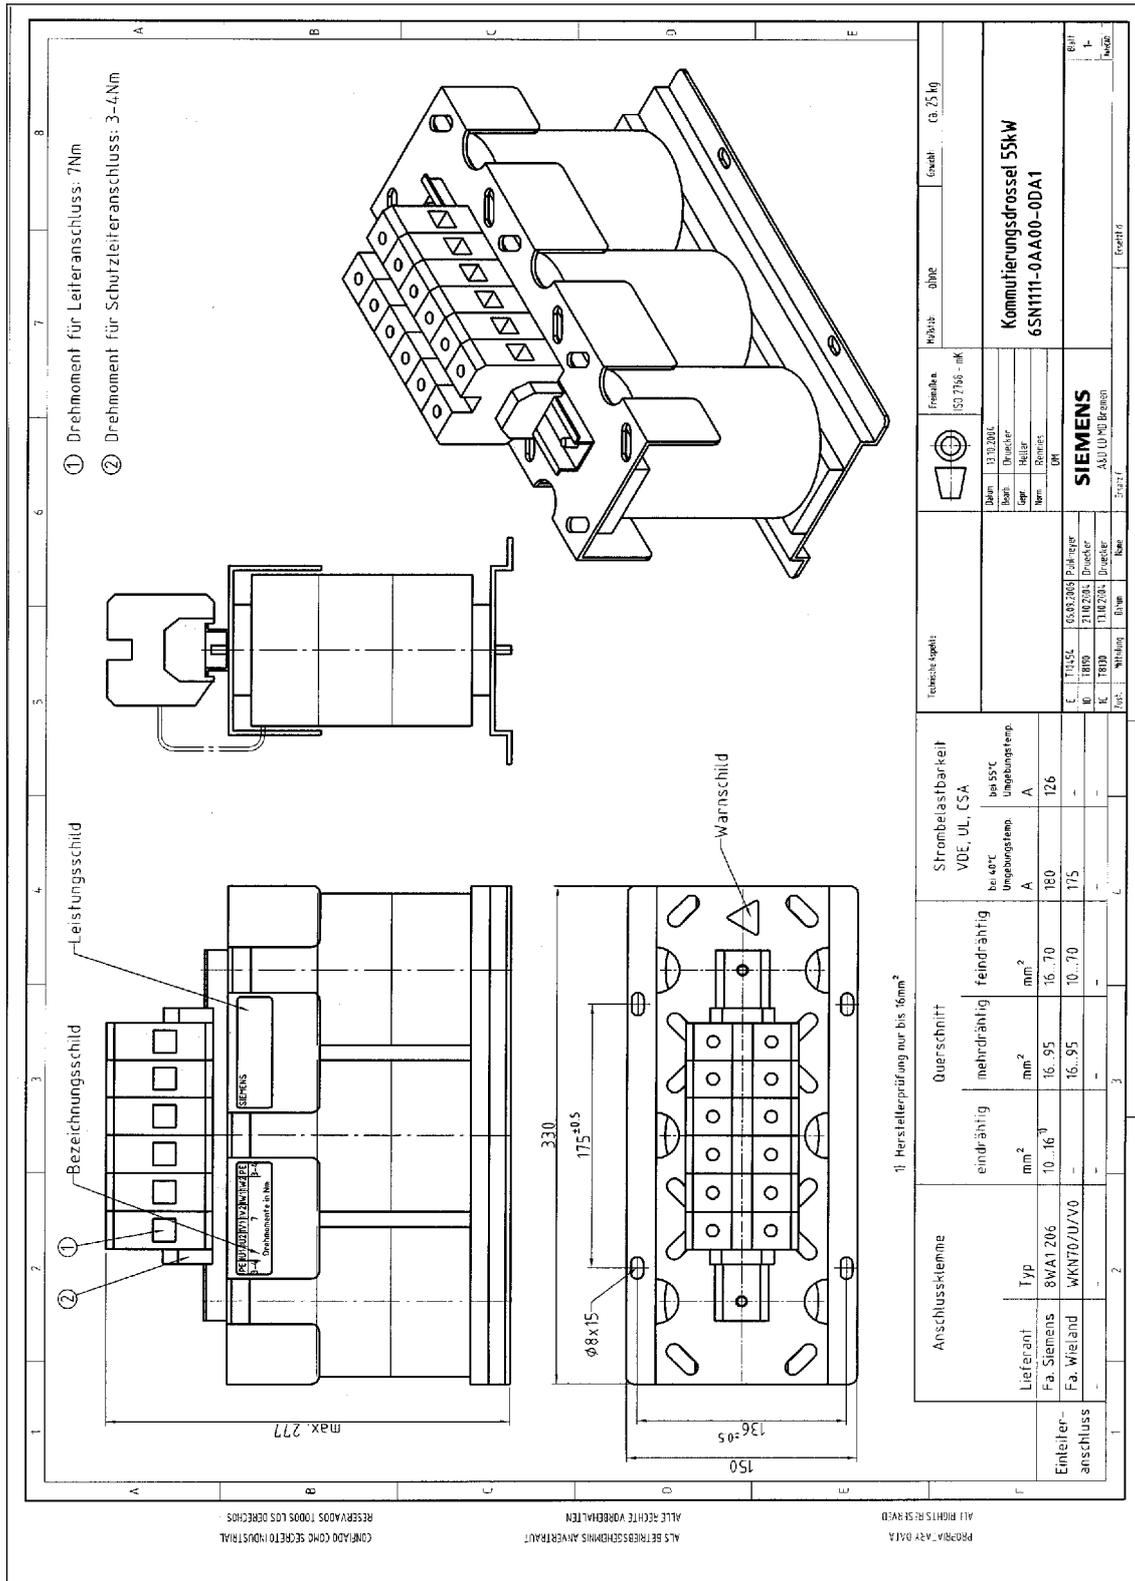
Bobina HF trifásica 55 kW, 6SN1111-0AA00-0DAx
